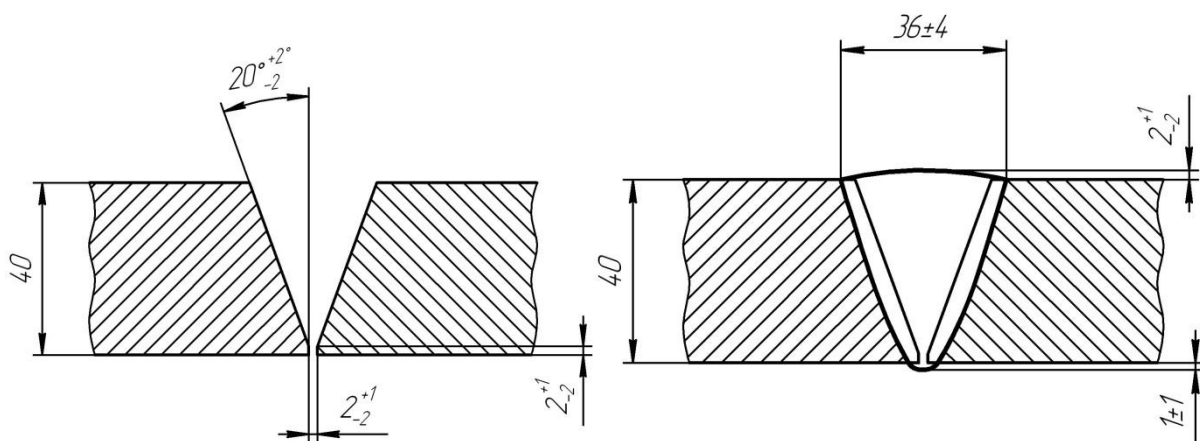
Подготовка кромок под сварку и вид сварного соединения
